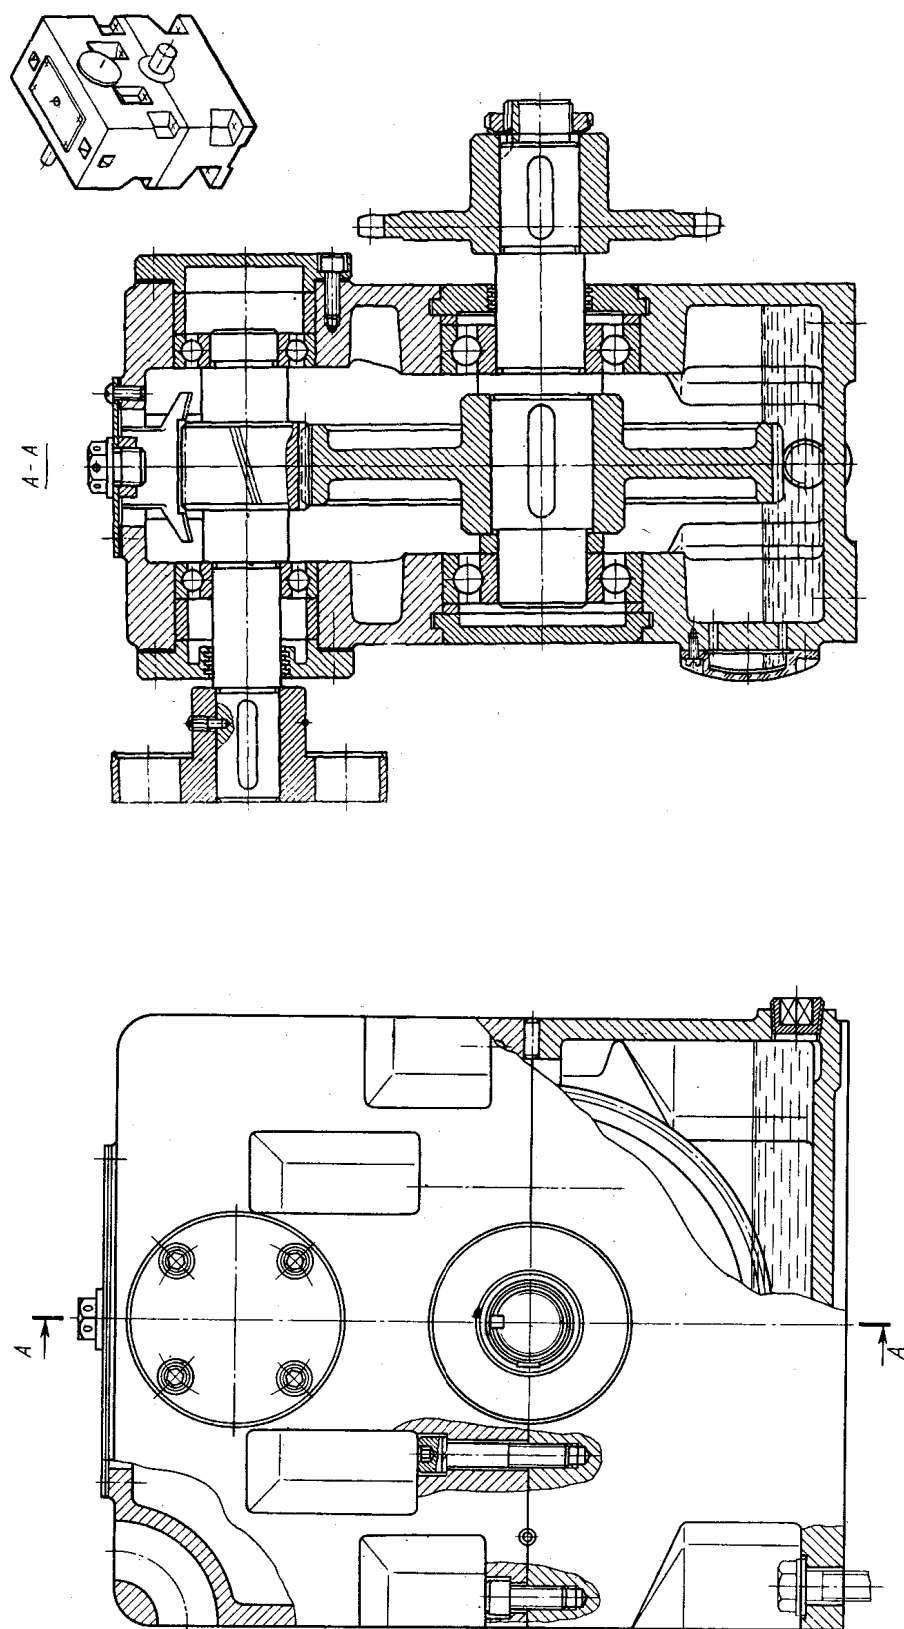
Редуктор (A11) цилиндрический одноступенчатый вертикальный с верхним расположением шестерни
